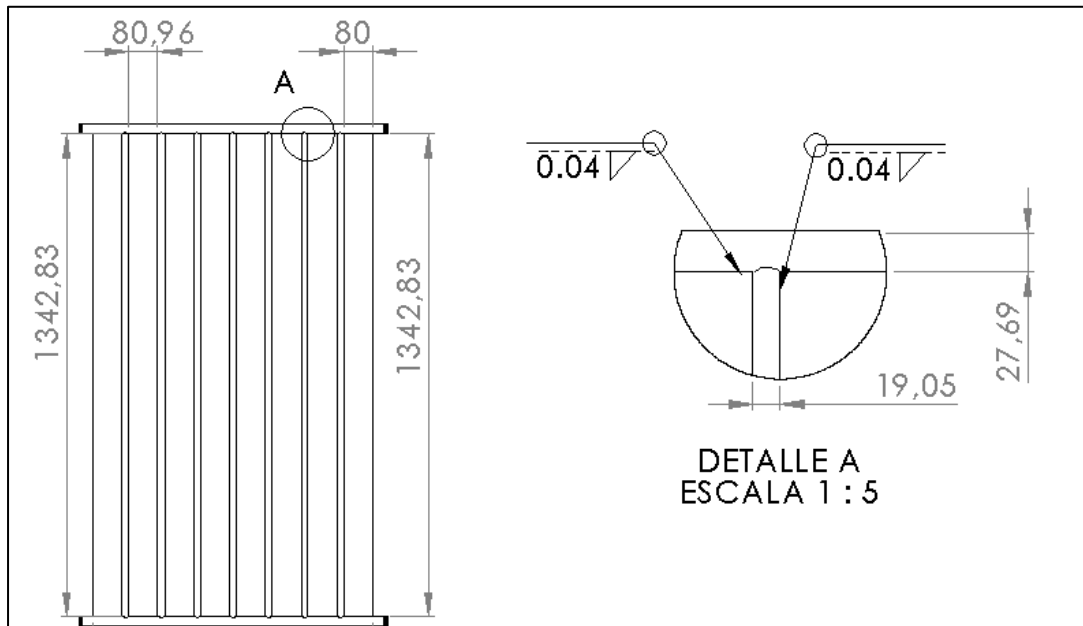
Dimensiones del conjunto de aletas soldadas.
